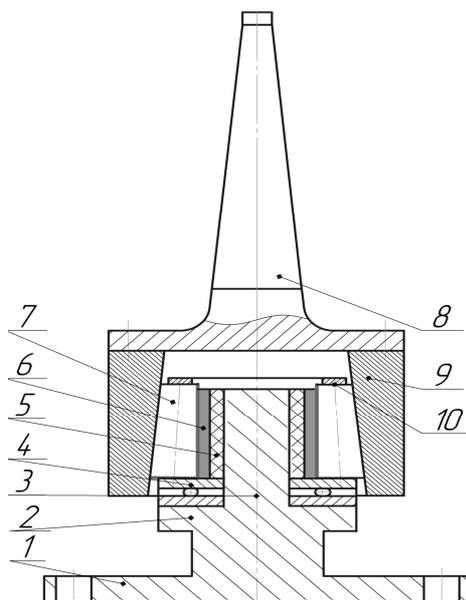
Многороликовая обкатка бронзовых подшипников скольжения: 1- нижняя платформа опоры- матрицы, 2- верхняя платформа опоры-матрицы, 3- ствол опоры-матрицы, 4- упорный подшипник, 5- гидропласт, 6- втулка для обжима, 7- деформирующий ролик, 8- нажимной конус, 9- коническая оправка, 10- сепаратор
